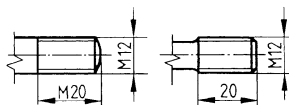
Gewindeauslauf nicht gezeichnet; liegt außerhalb der Abschlusslinie bzw. des Gewindelängenmaßes (der nutzbaren Gewindelänge)
